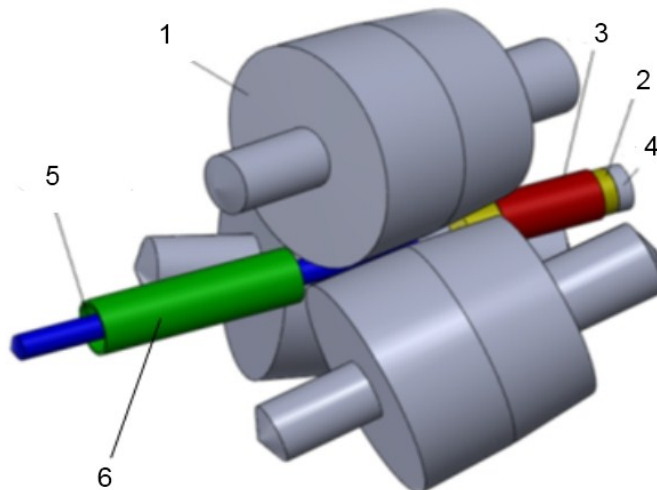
Сборка, созданная в SolidWorks: 1 – валок; 2 – заготовка; 3 – проводка; 4 – толкатель; 5 – оправка; 6 – проводка
